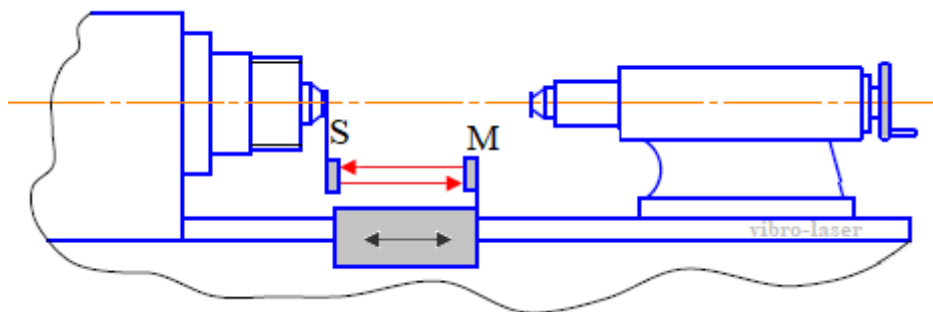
Установка лазерных головок S и М системы лазерной центровки
